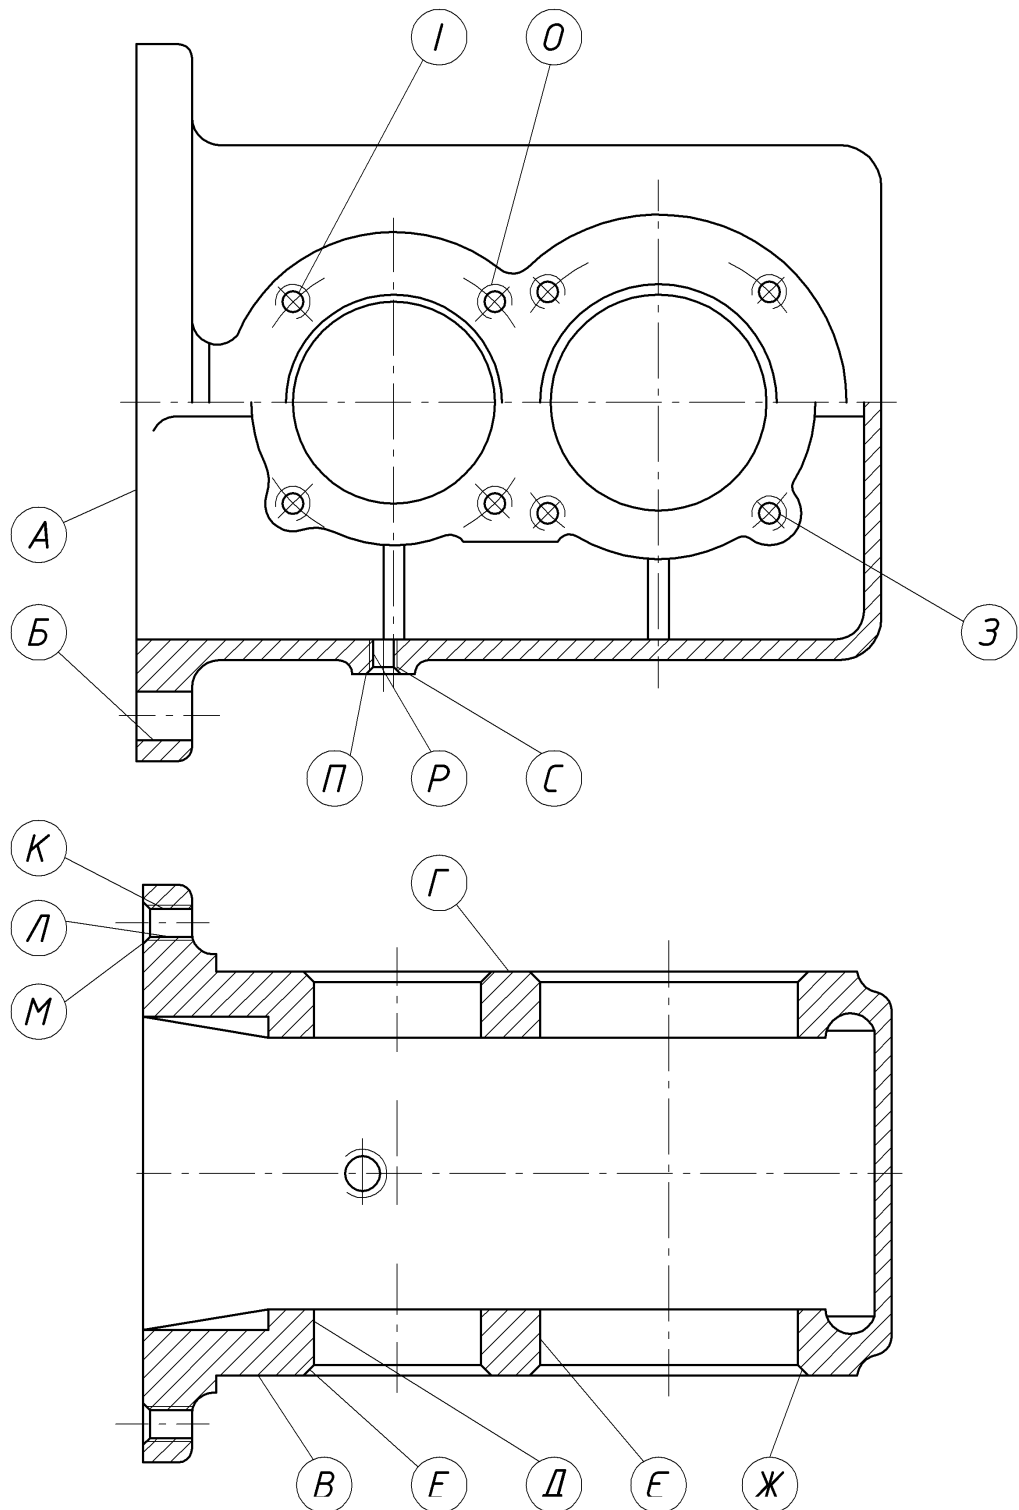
Схема розташування поверхонь корпусу КС6Б-53.102
